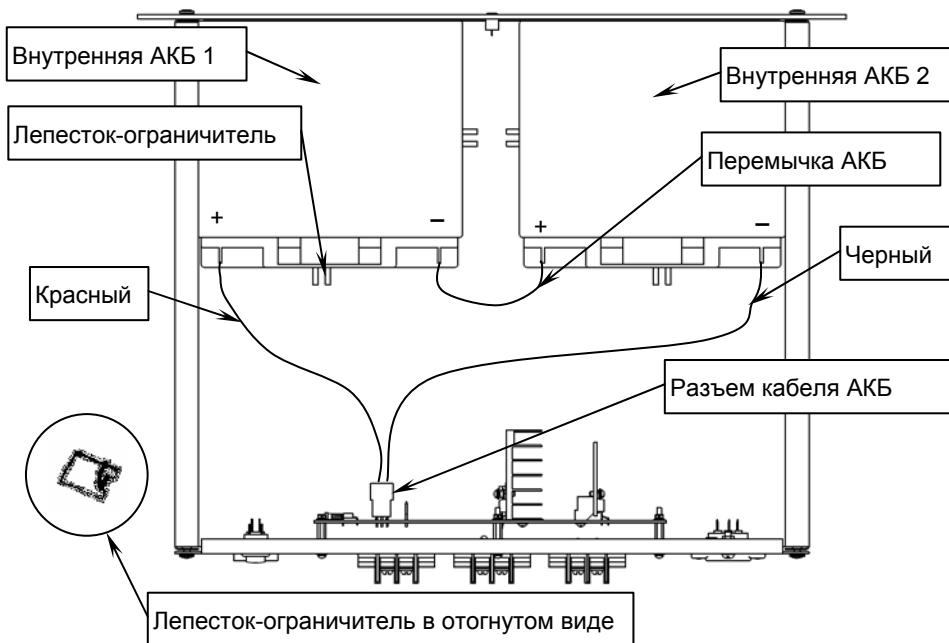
Вид изделия со снятой крышкой и установленными АКБ
